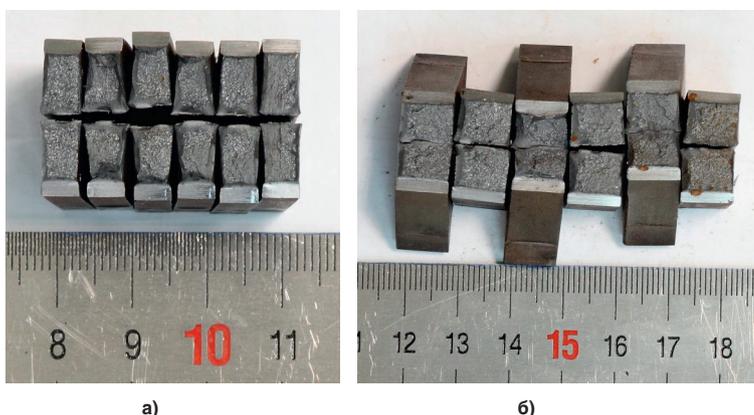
Поверхность излома образцов стыковых сварных соединений пластин: а) 09Г2С (К52) толщиной 8 мм; б) 10Г2ФБЮ (К60) толщиной 16 мм
